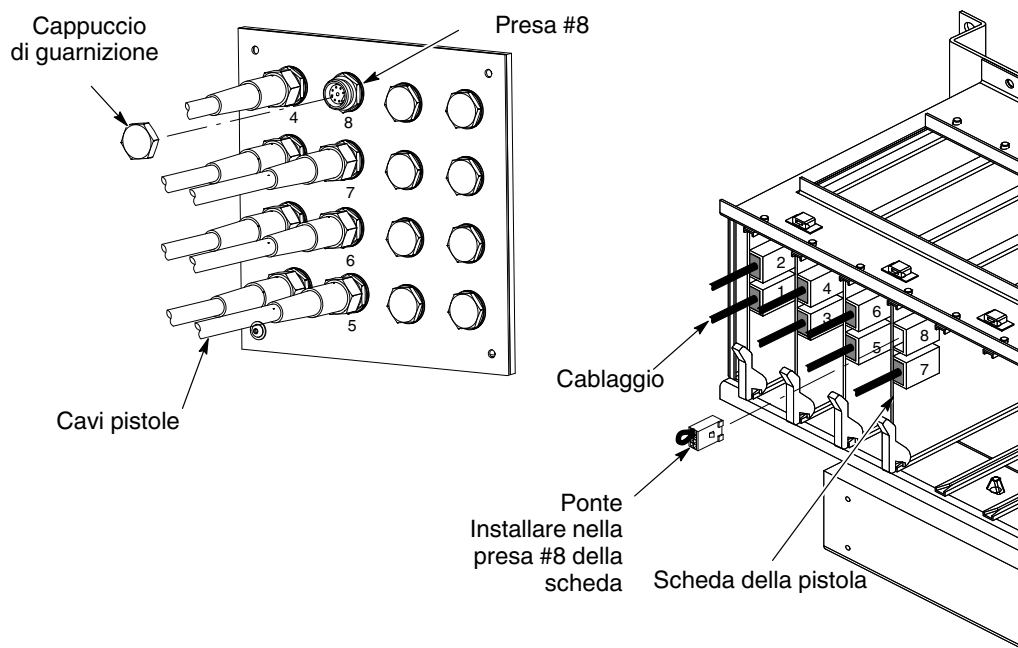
Installazione di guarnizione e ponte - Esempio di sistema da 8 pistole che impiega 7 pistole
